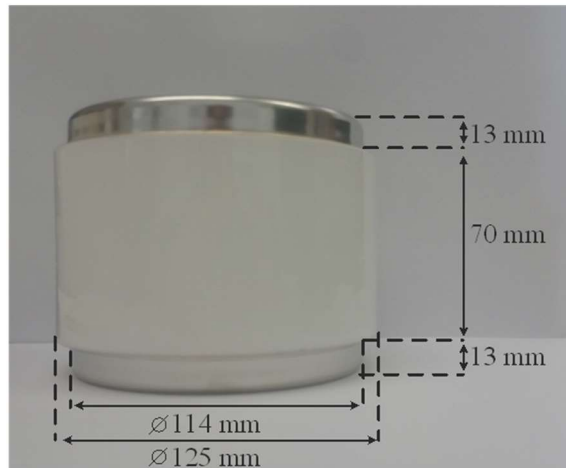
Prüfkörper mit äußeren Abmessungen
